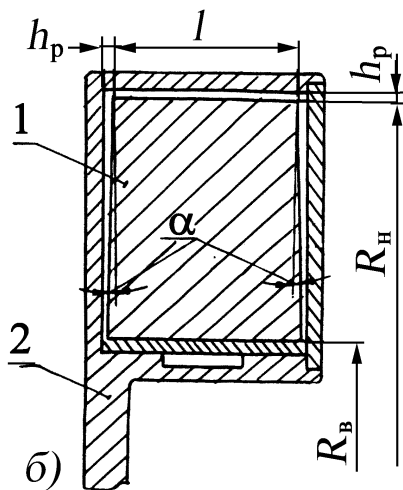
Схема жидкостного демпфера: 1 – маховик; 2 – корпус; а – торцевые зазоры постоянные; б – торцевые зазоры конические
